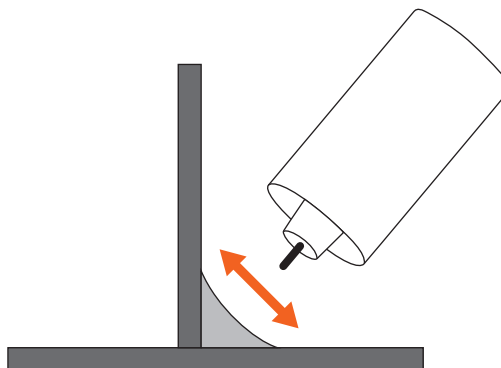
Качание сварочной головки в процессе TAST
